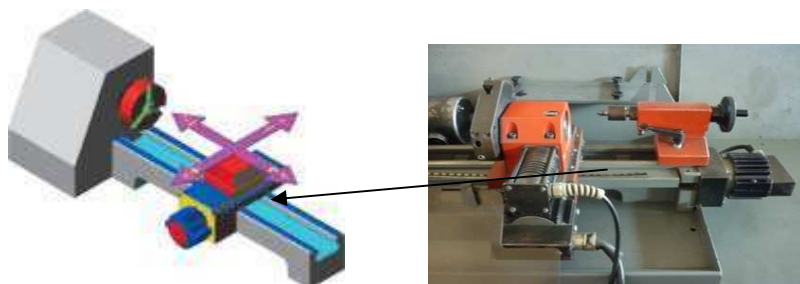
Motor Utama Mesin bubut CNC TU-2A
